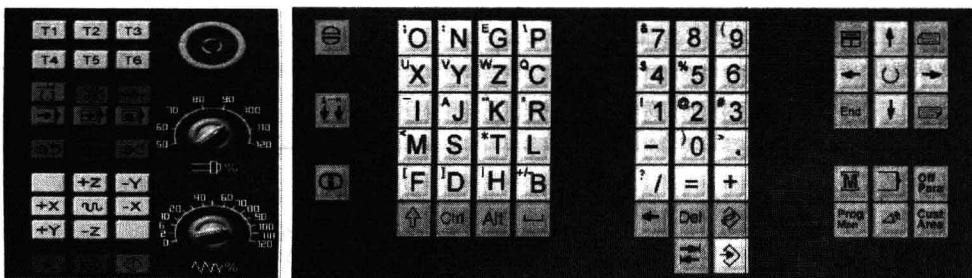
SIEMENS 802D 数控铣床/加工中心机床操作面板及系统面板
